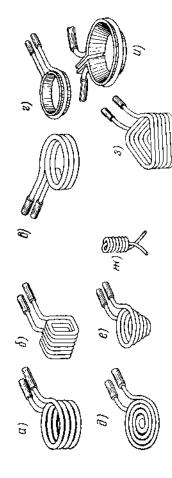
Различные конструкции индукторов, применяемых для натрева под пайку:
